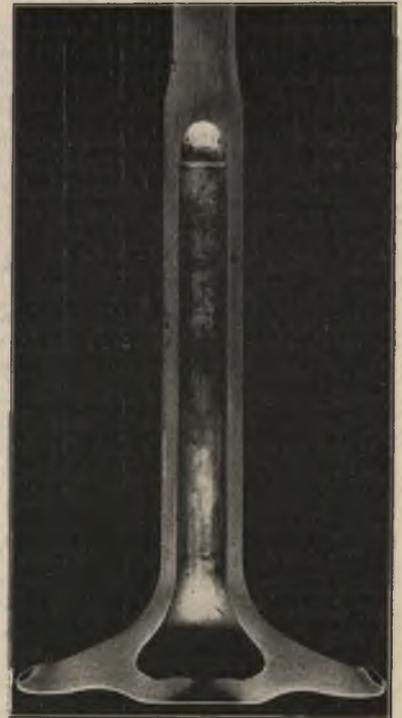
(rechts). Auslaßventil eines deutschen Flugmotors mit halbhohlem Kopf und zugeschweißter Bodenbohrung für die Füllung mit Natrium. (× rd. 0,85.)
